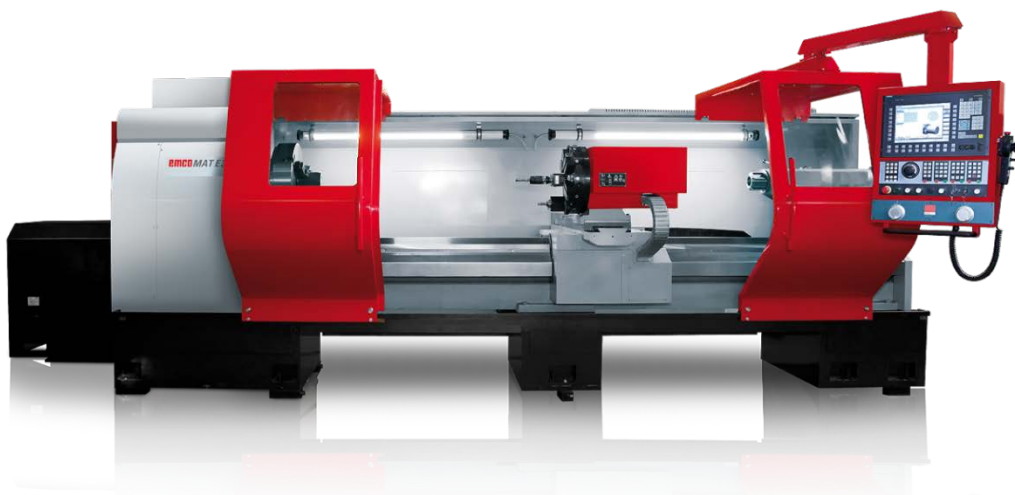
Токарно-винторезный станок EMCOMAT E-360
